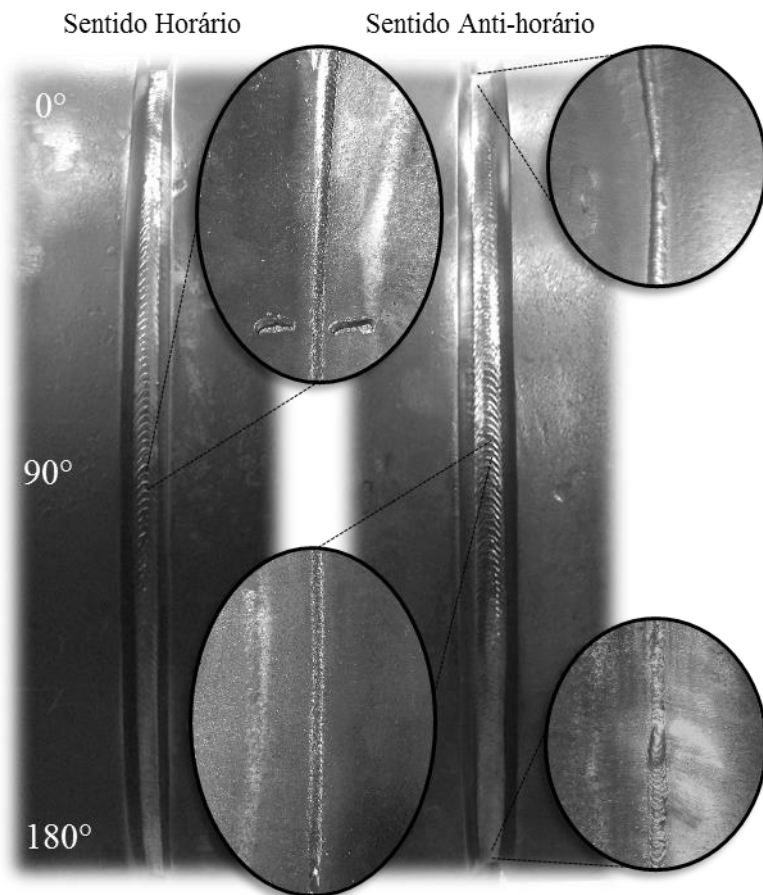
Corpo de prova 1 da matriz de ensaios com solda.
